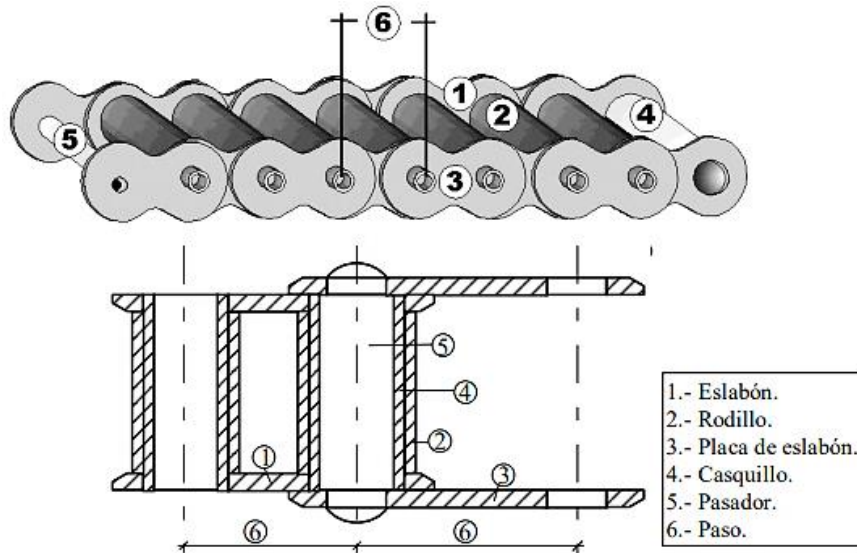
Partes de la cadena de rodillos. Tomada de Renold.es
